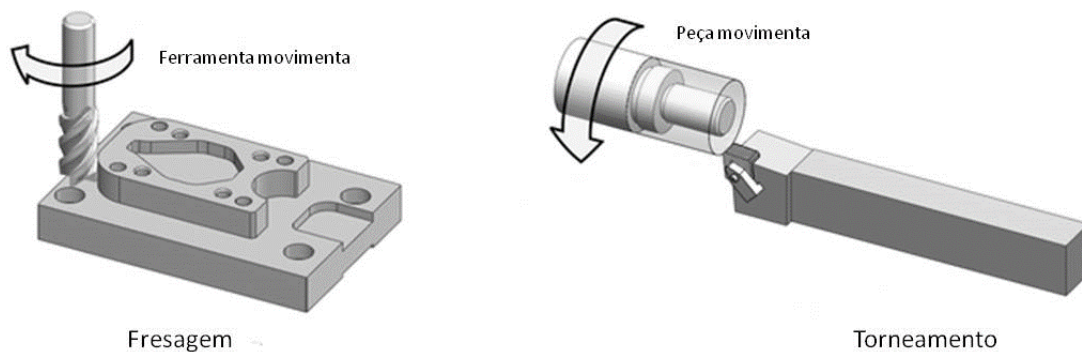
Exemplos das principais diferenças de torneamento e fresagem.
